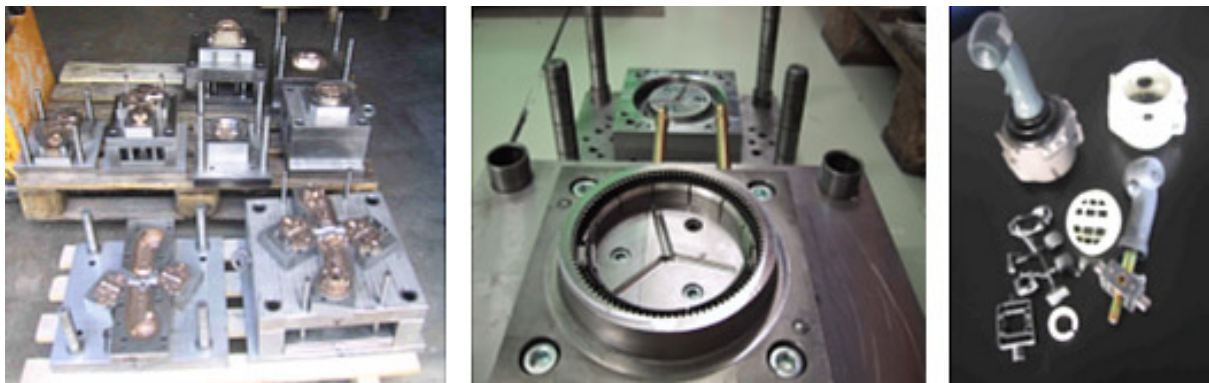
Spritzgusswerkzeuge und Funktionsbauteile
